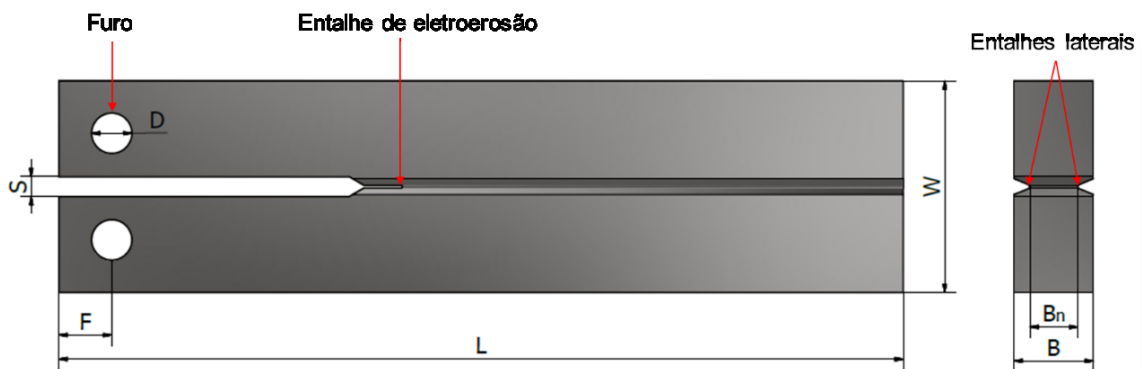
Desenho esquemático do corpo de prova DCB e suas principais dimensões.
